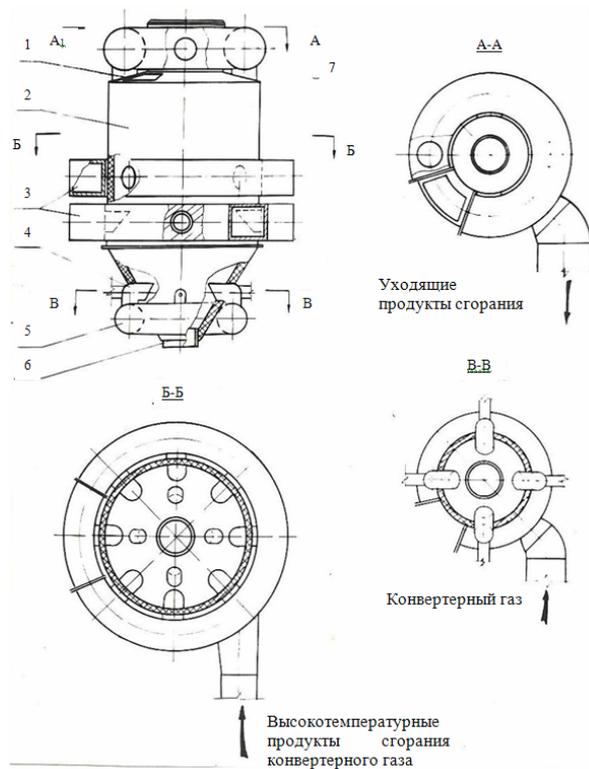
Общий вид реактора для обжига известняка конвертерным газом в противотоке
